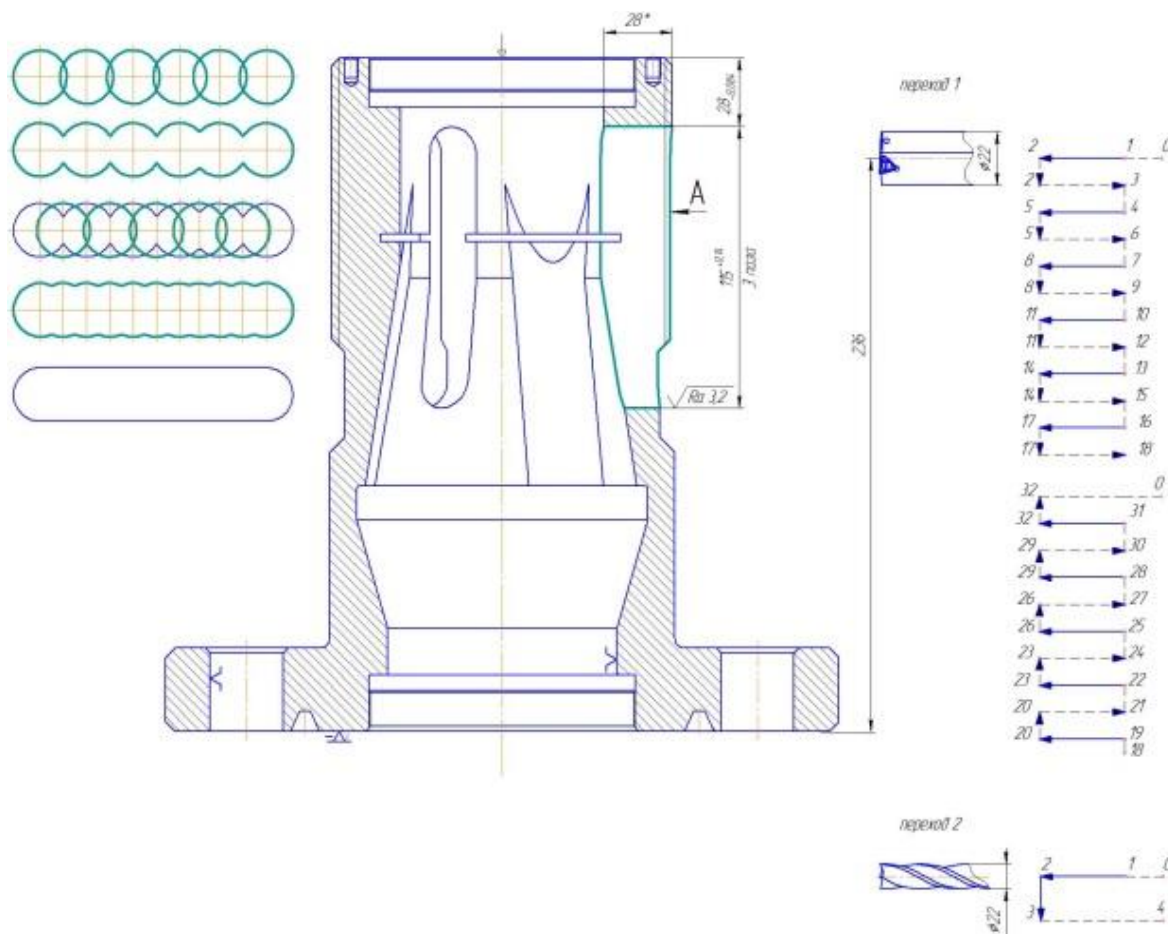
Плунжерное сверление при изготовлении направляющих пазов корпуса катушки шлицевой
